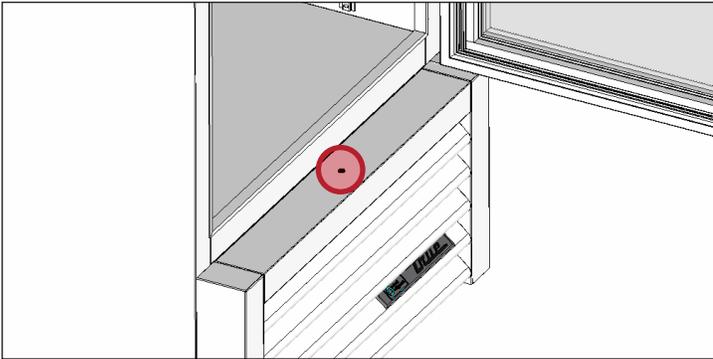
Porte à battant : Emplacement des vis de la grille de ventilation avant.
